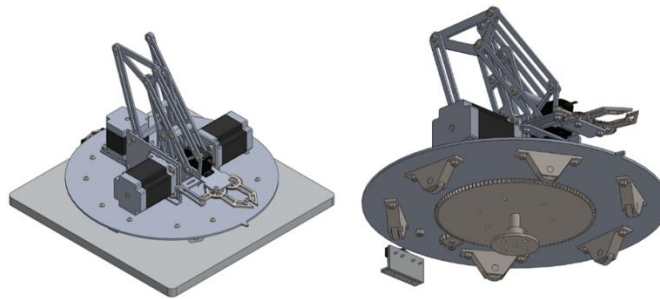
Vista isométrica e inferior del diseño 3D de la versión final
